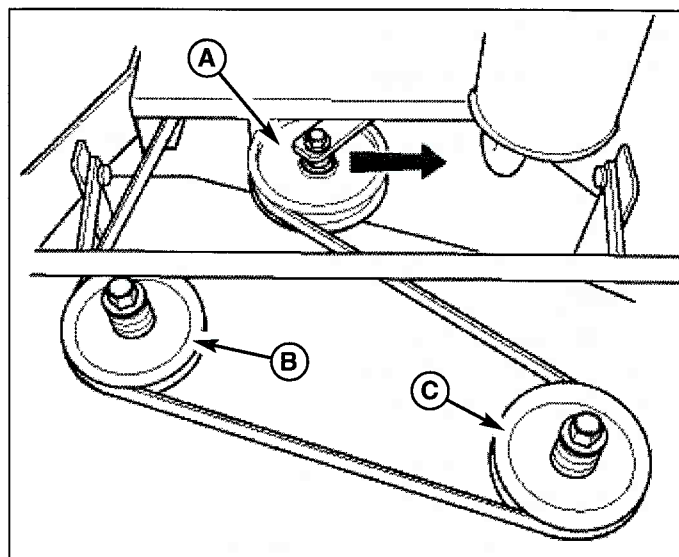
Courroie d'entraînement de la plateforme de la tondeuse
